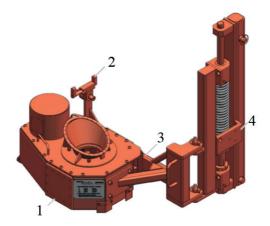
Safe-T-Spin: 1 – система безопасного вращения; 2 – запирающий механизм; 3 – опорный рычаг; 4 – мачтовая насадка в сборе
